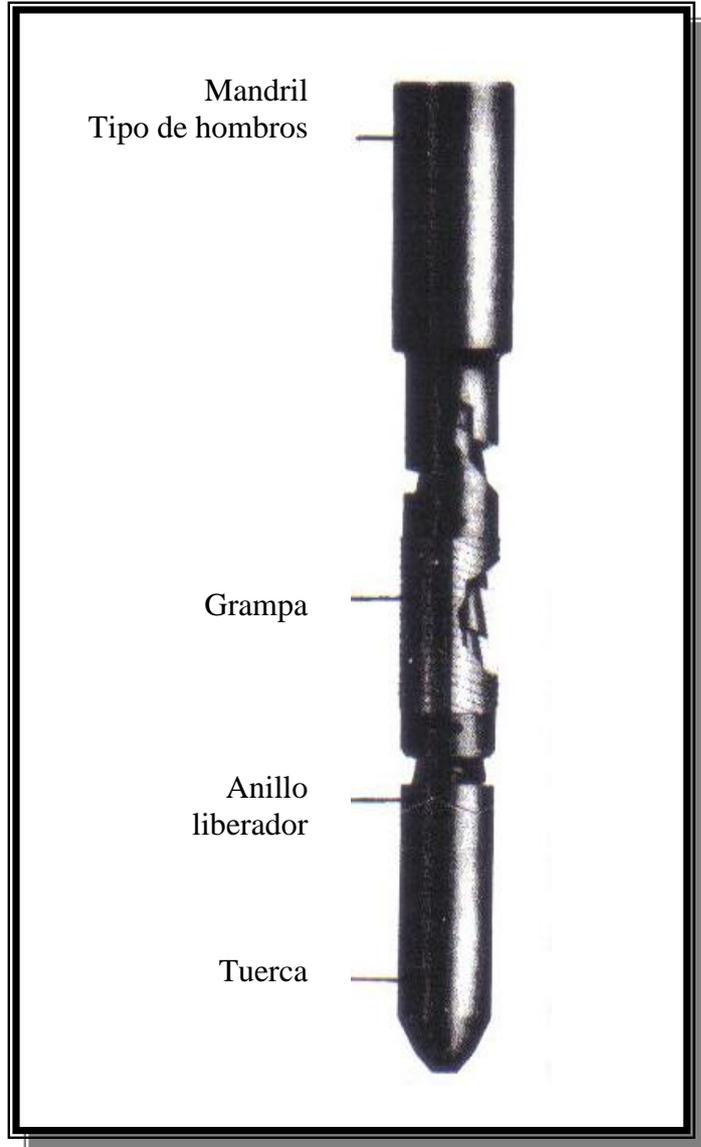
"Releasing Spear" tipo de hombros; fuente: Bowen Fishing tools Technical Manual No.2300.
